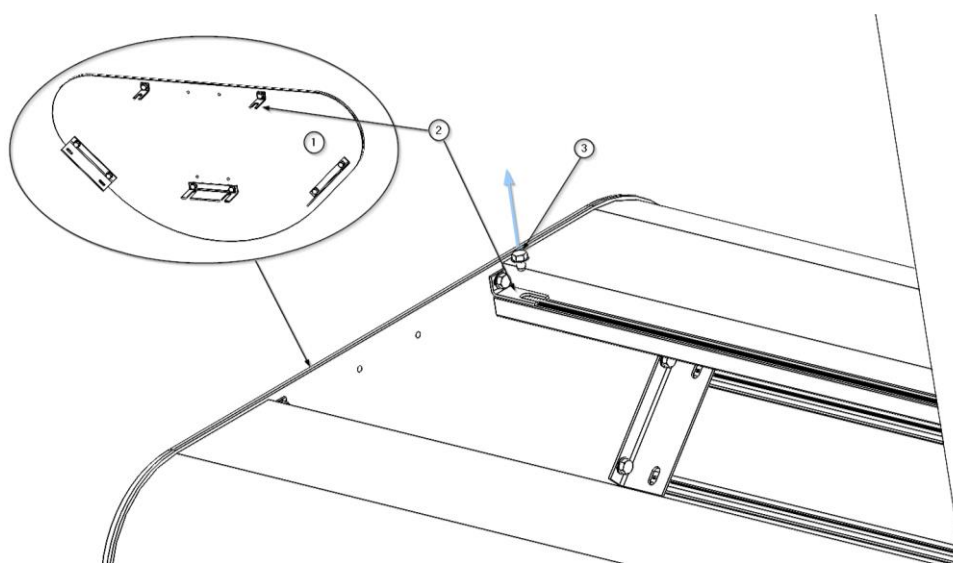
Démontage/montage des embouts sur le corps principal de l'ARES
